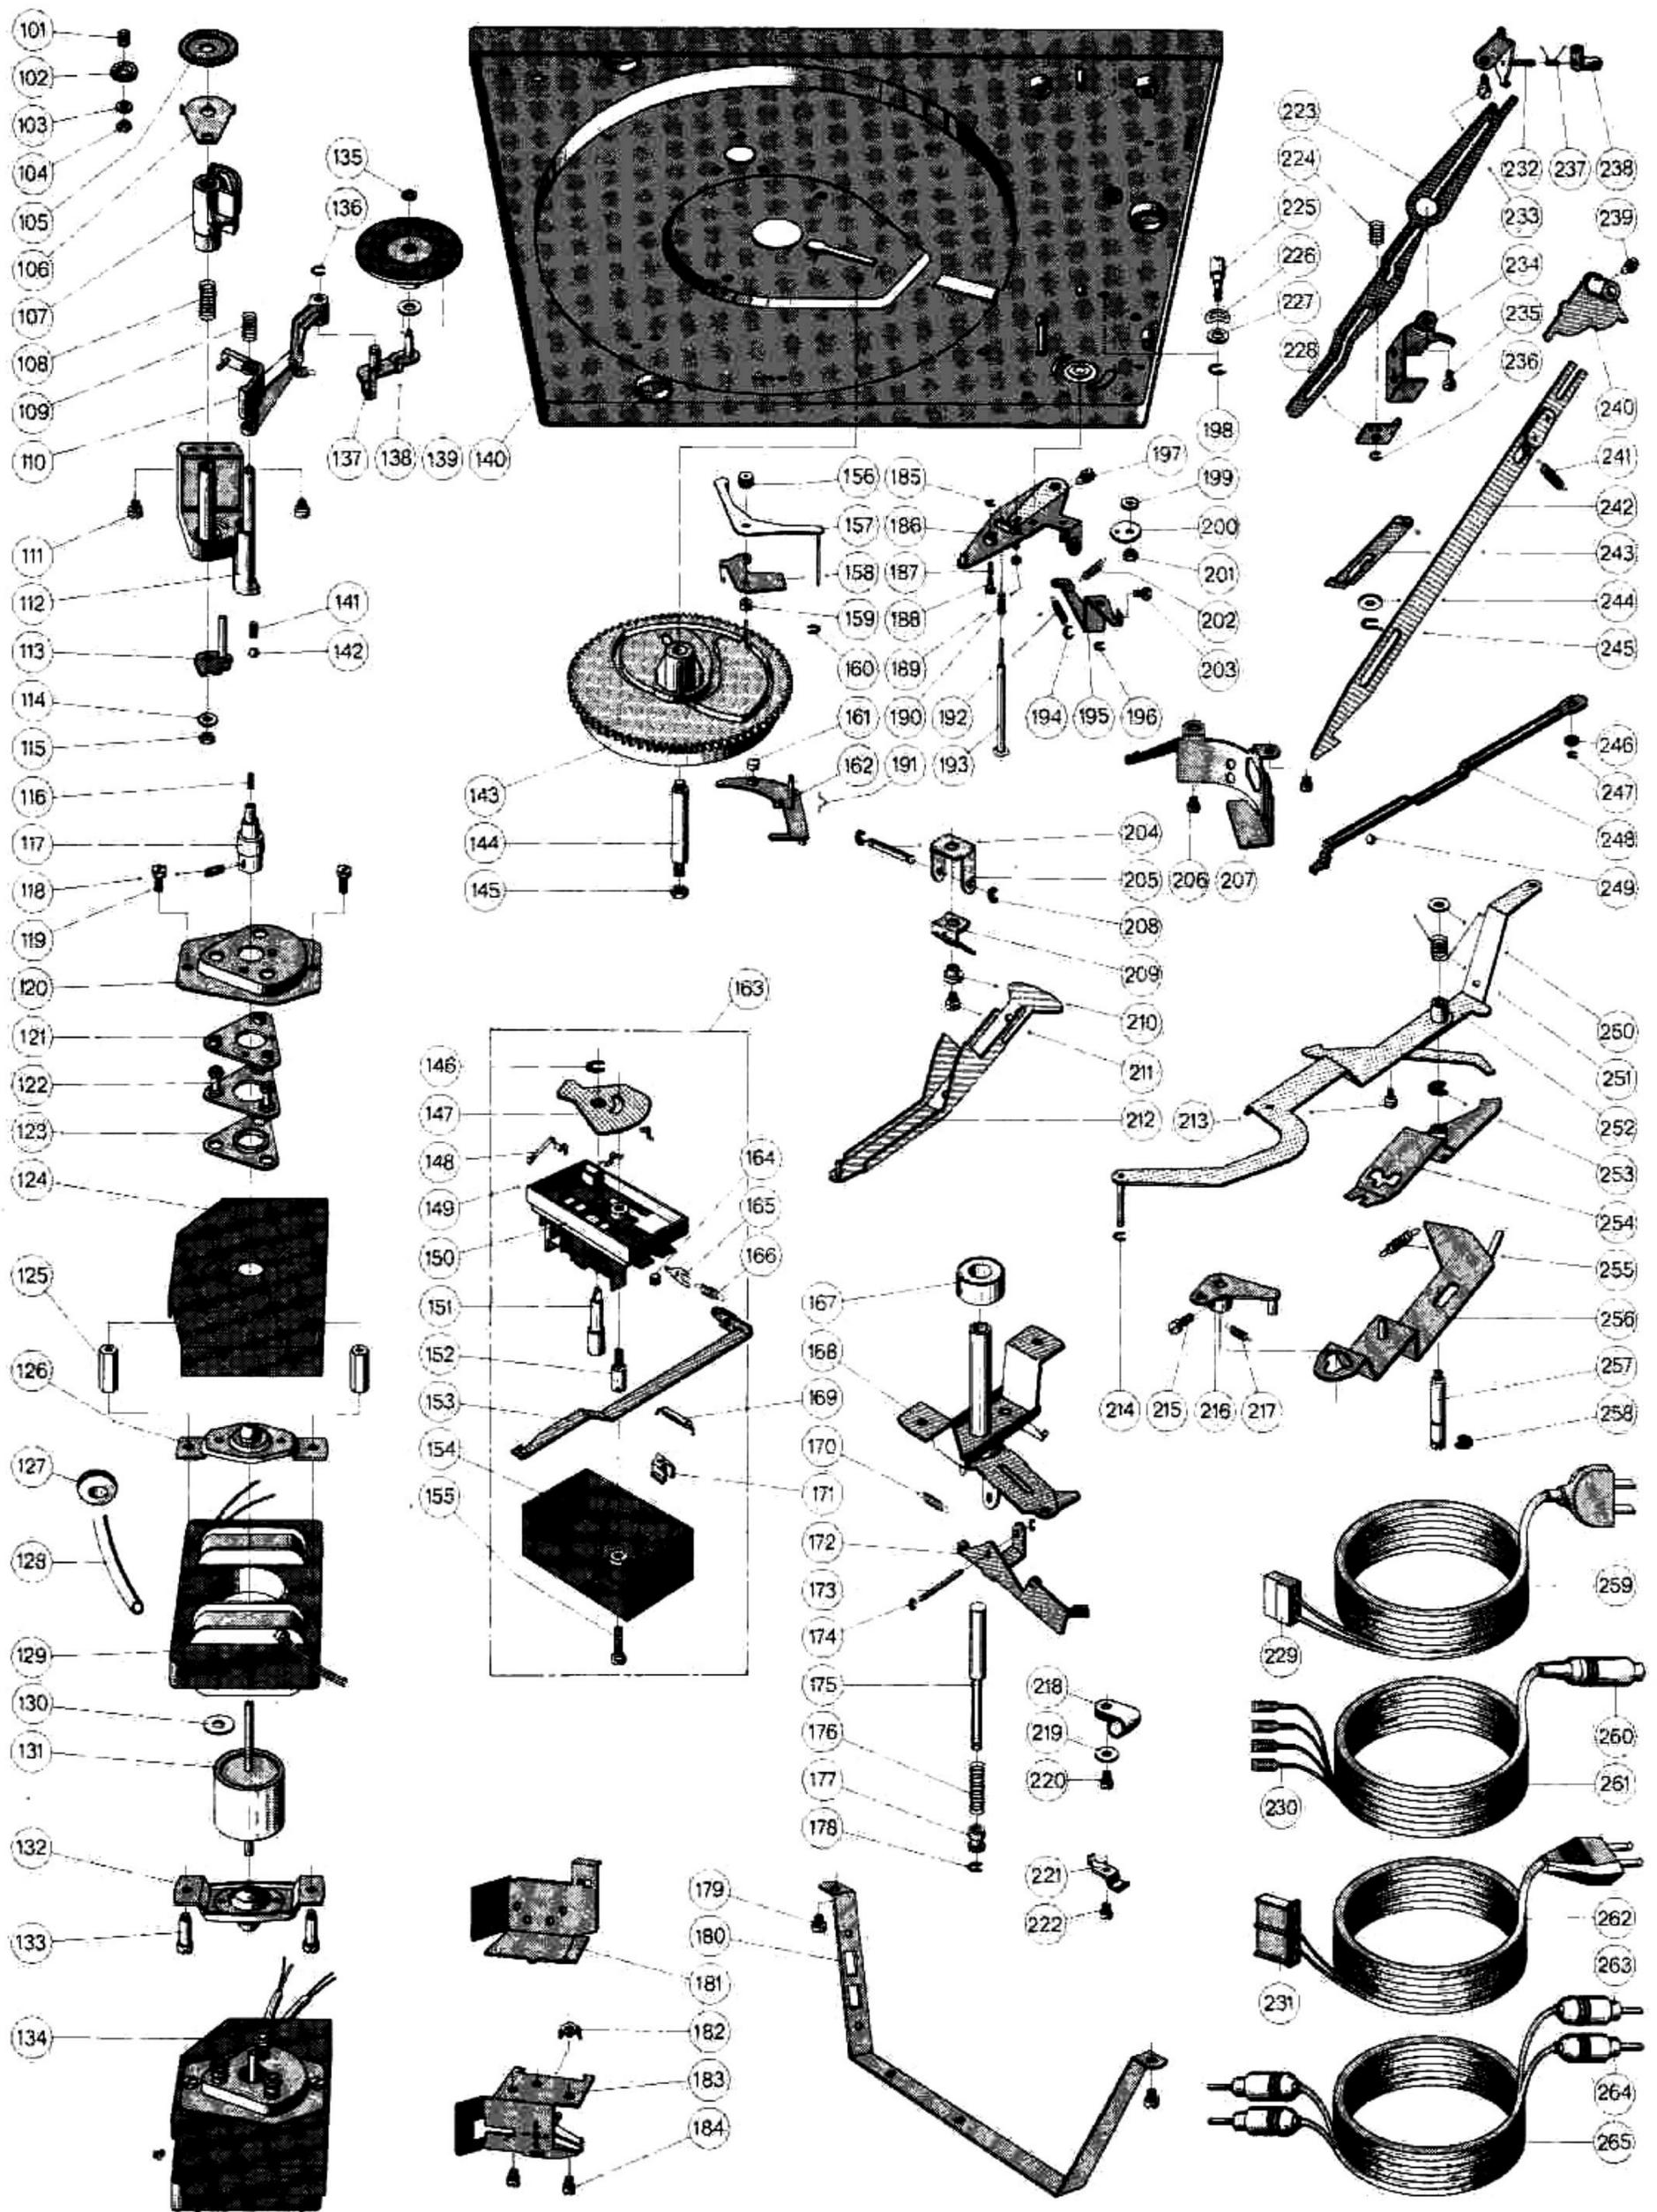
Représentation explosée, pièces en-dessous de la platine
